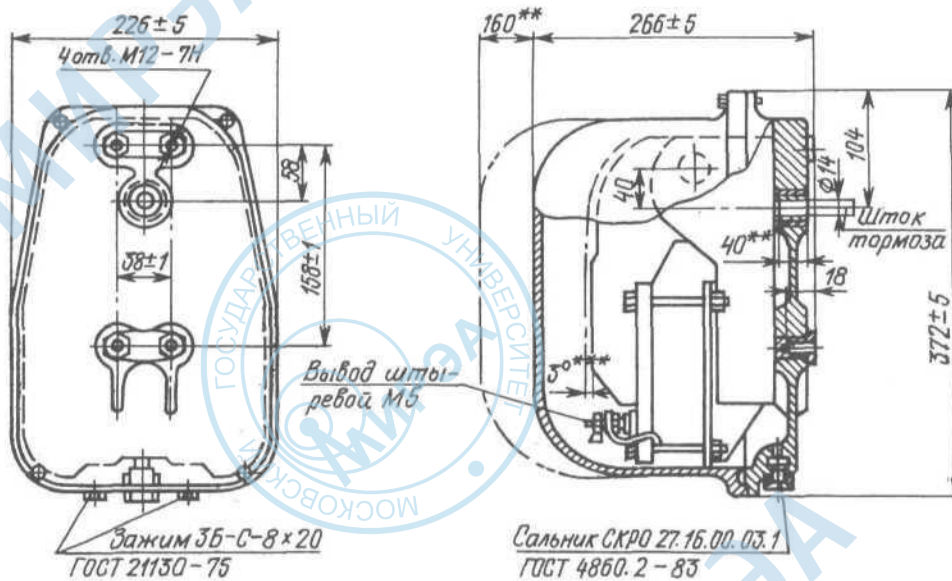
Габаритные и установочные размеры электромагнита типа MOM-210
